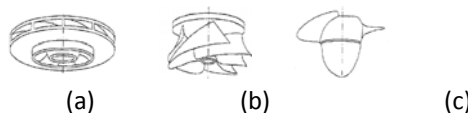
Rotores de bombas: (a) Rotor radial; (b) Rotor misto, (c) Rotor axial (fonte: <http://www.poli.usp.br>).
